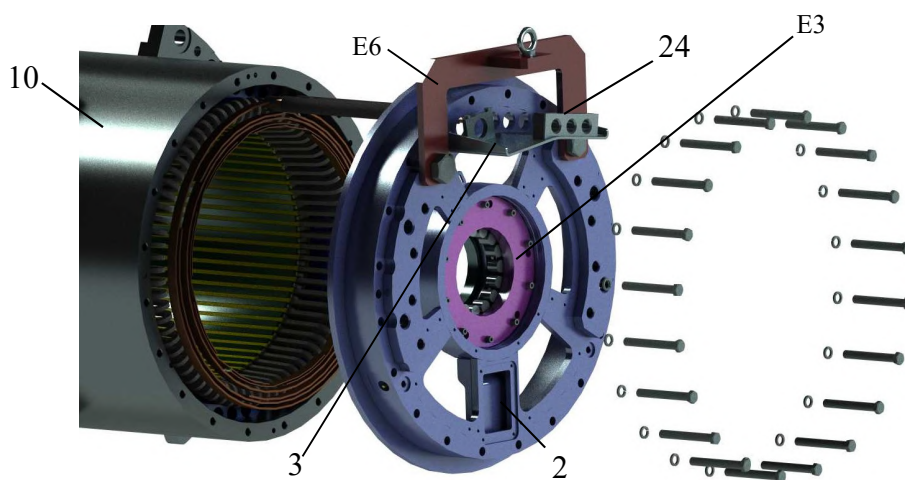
Монтаж щита подшипникового со стороны тормоза
